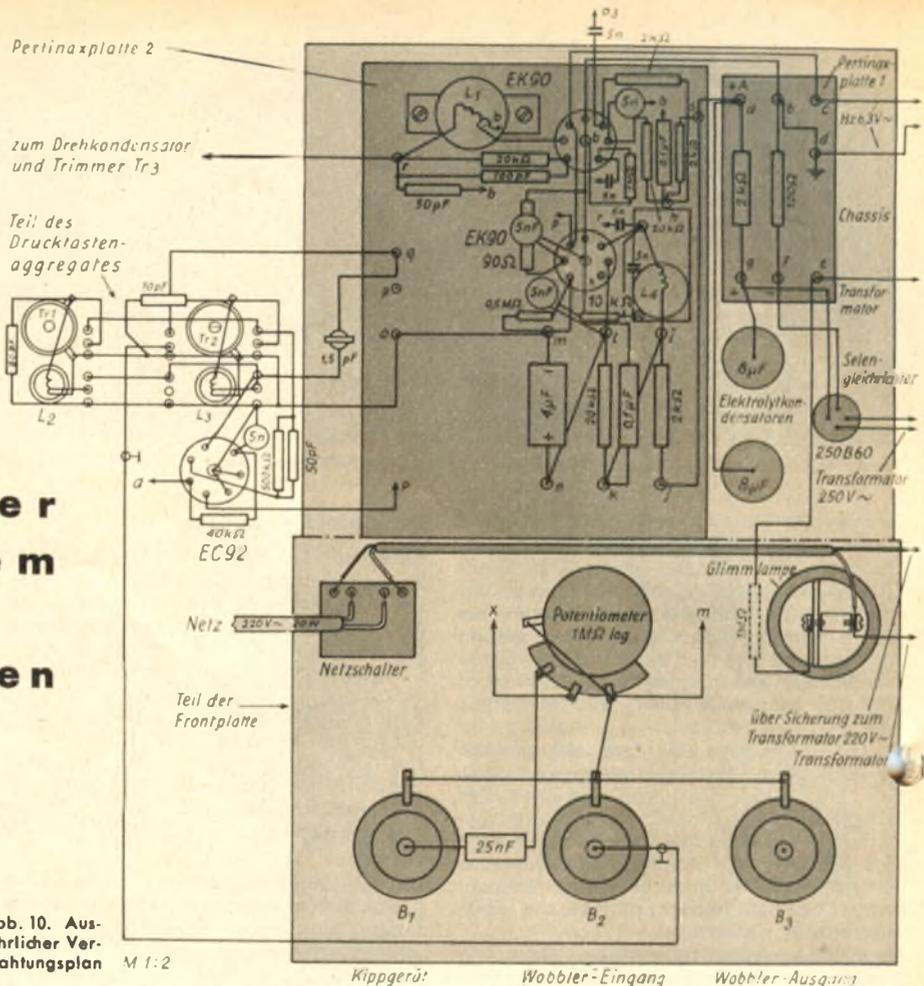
Ausführlicher Verdrahtungsplan M 1:2
